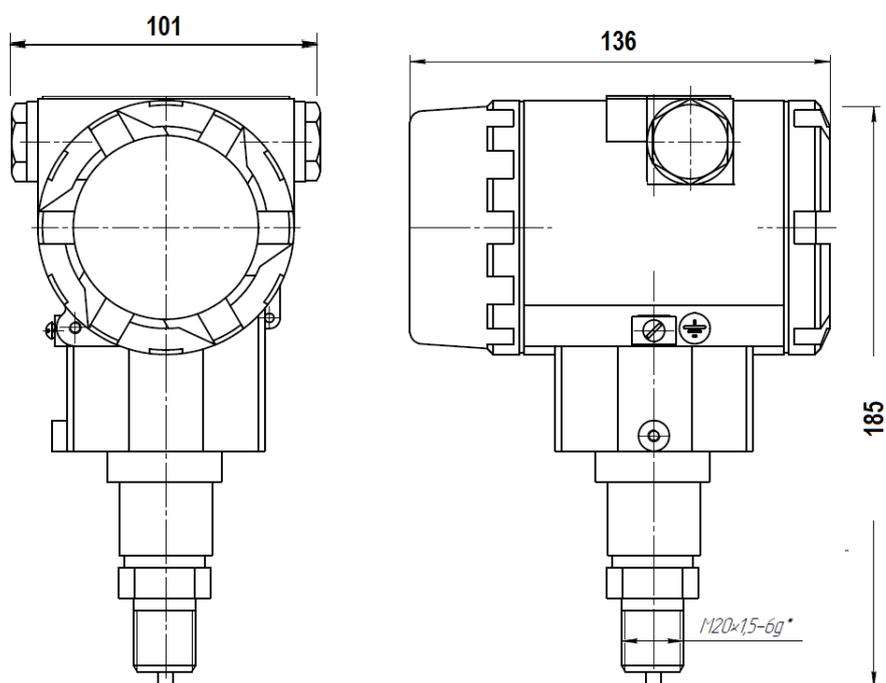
Габаритные и установочные размеры датчиков абсолютного и избыточного давления
